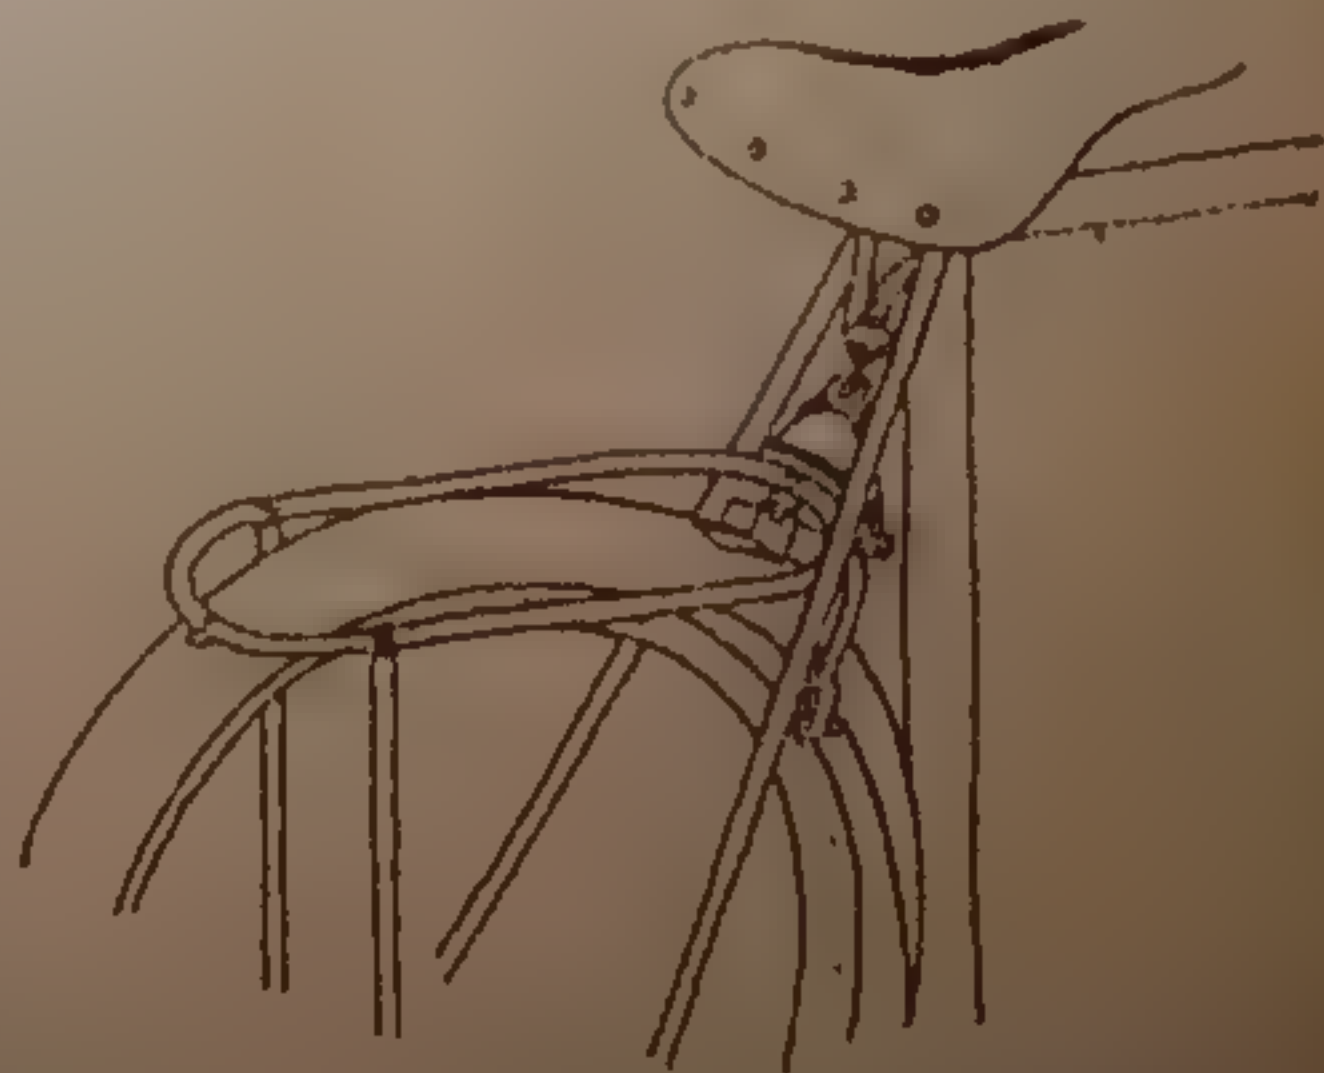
Крепление багажника из дюралюминиевых трубок.
